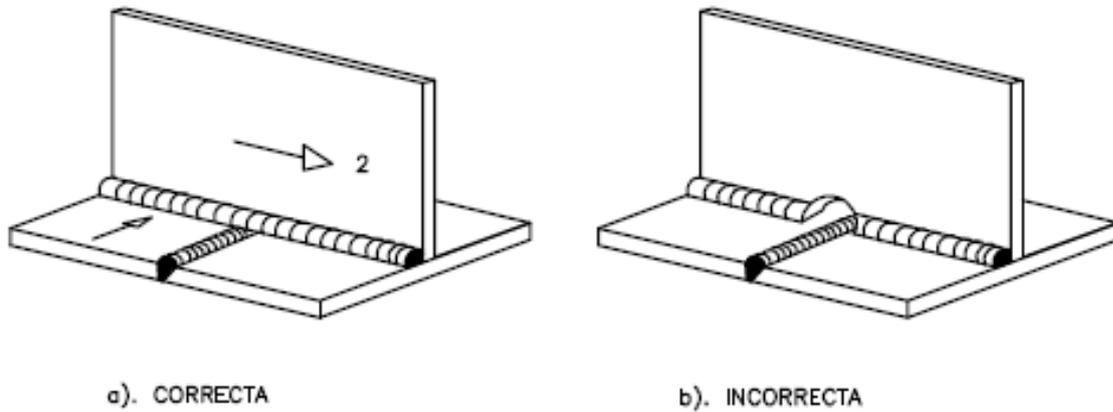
Uniones en ángulo con soldaduras cruzadas (dos cordones).
